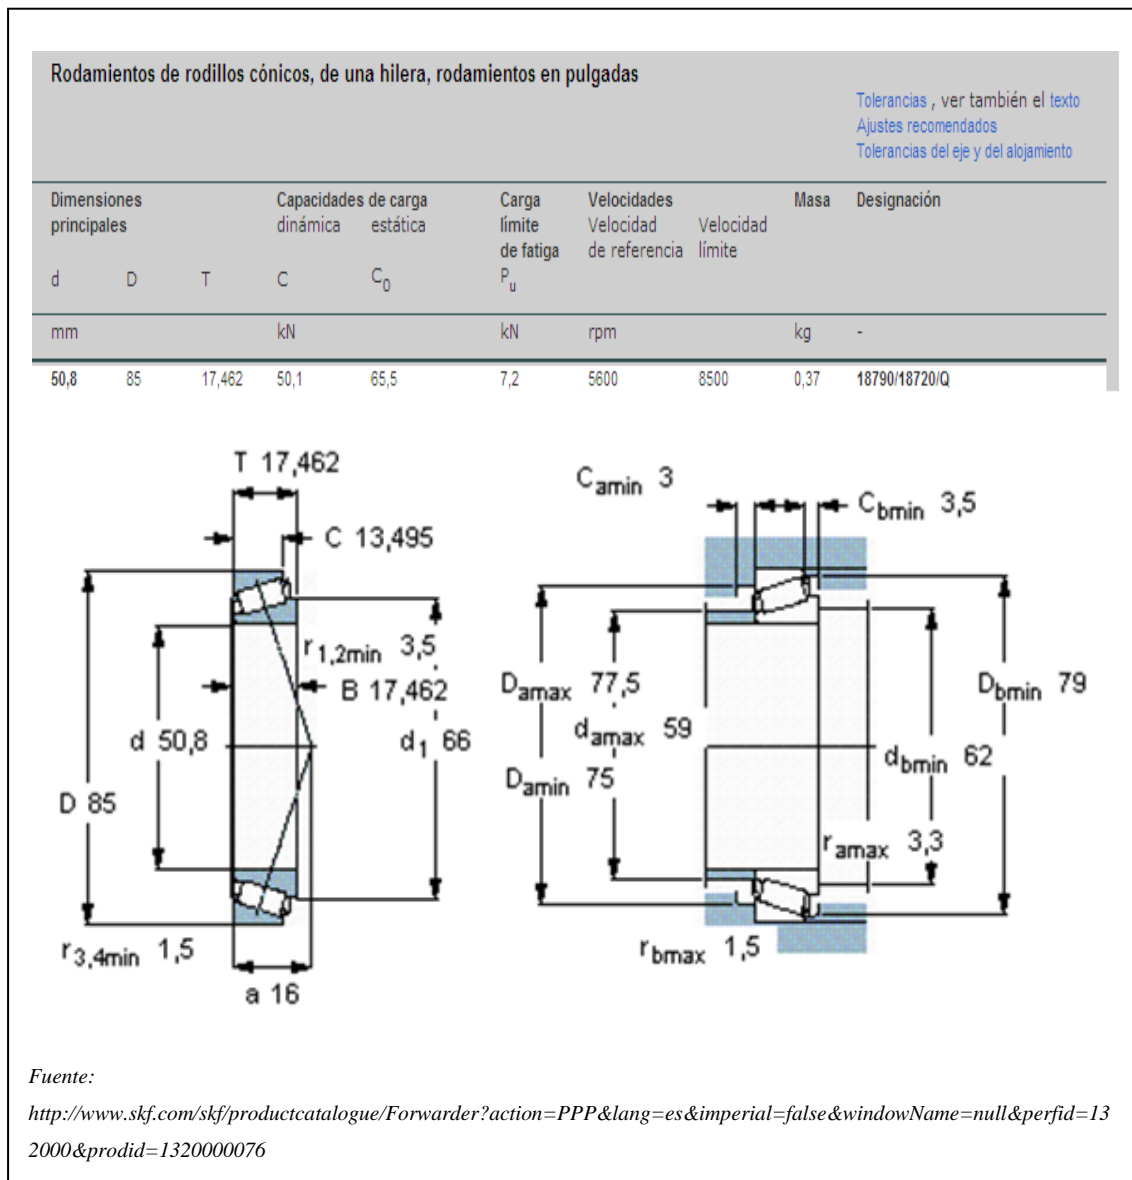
Características del Rodamiento de Rodillos Cónicos Seleccionado Ø2”
